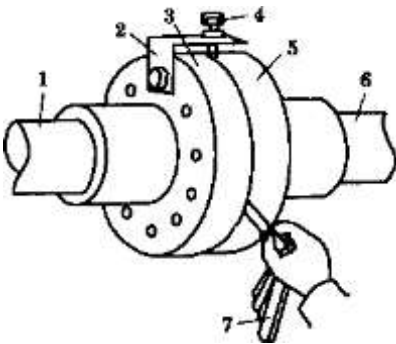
Центровка валов методом обхода одной точкой: 1 — вал двигателя; 2 — центровочная скоба; 3 — полумуфта двигателя; 4 — штифт; 5 — полумуфта приводного механизма; 6 — вал приводного механизма; 7 — щуп
